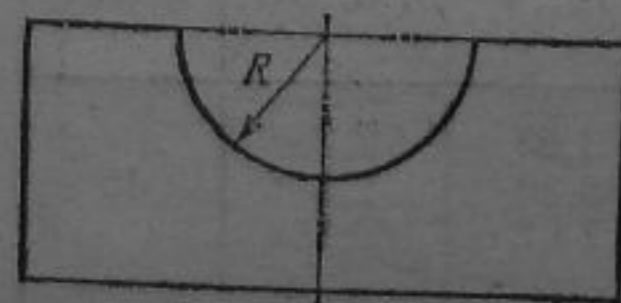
Эскиз обрабатываемой поверхности заготовки к задаче 65
